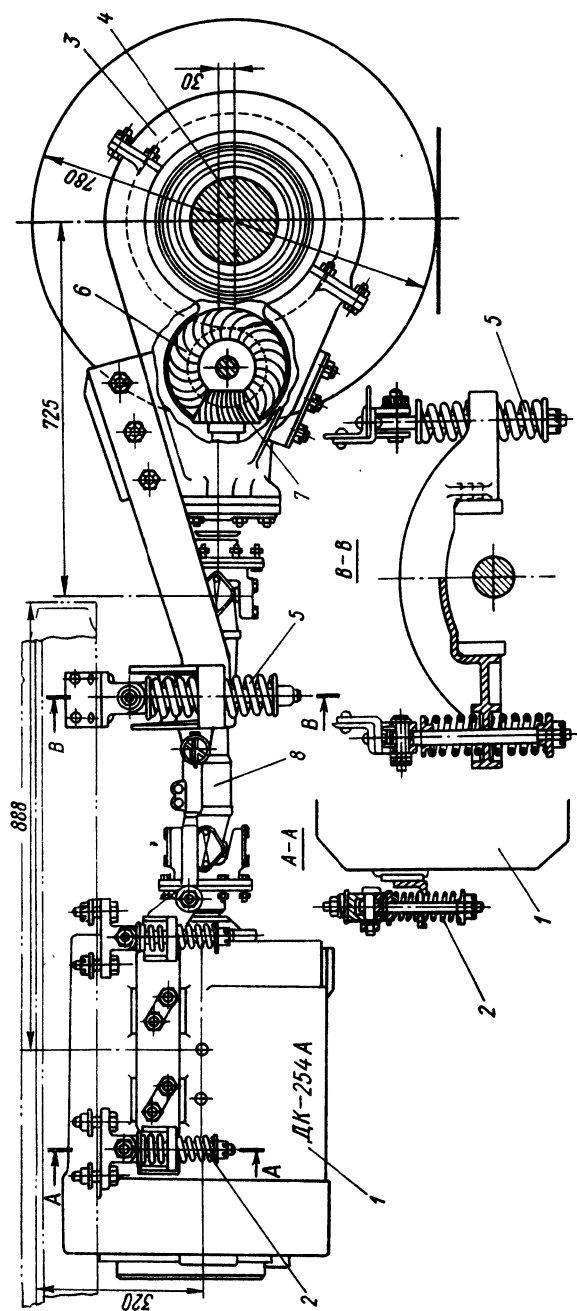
Привод через зубчатый редуктор от двигателя с независимой подвеской
